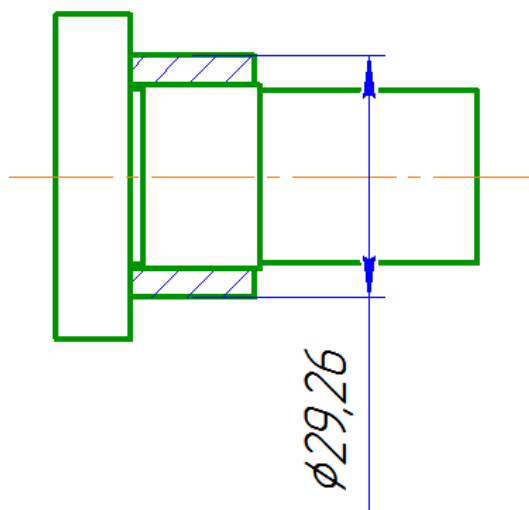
Примеры эскизы деталей до и после запрессовки
